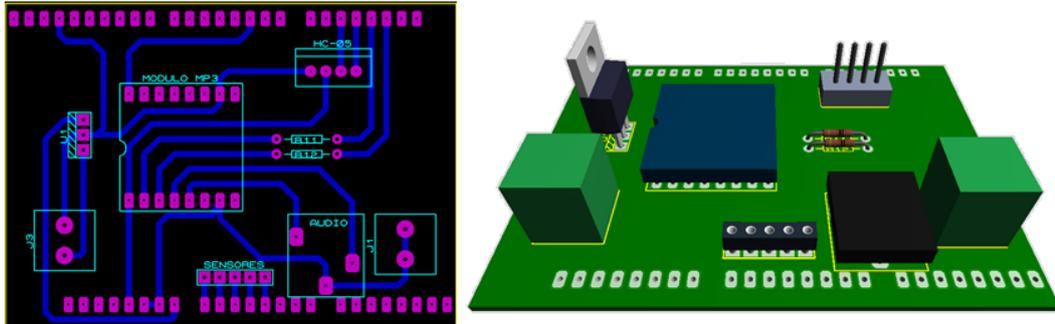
Diseño de la PCB del Módulo Baño Interactivo
